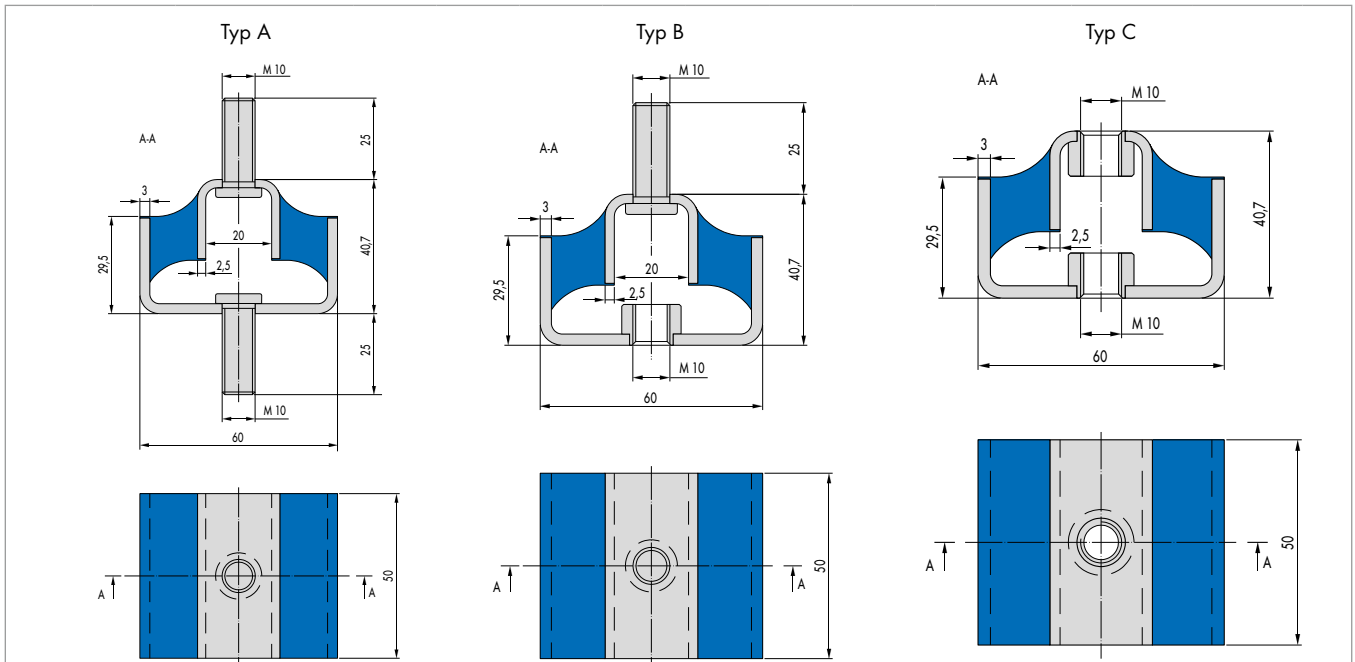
Doppel-U-Lager 053 18 702, 053 18 703 und 053 18 704
